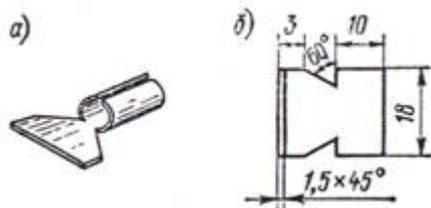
Демонтажная насадка (а) и развертка заготовки (б).
